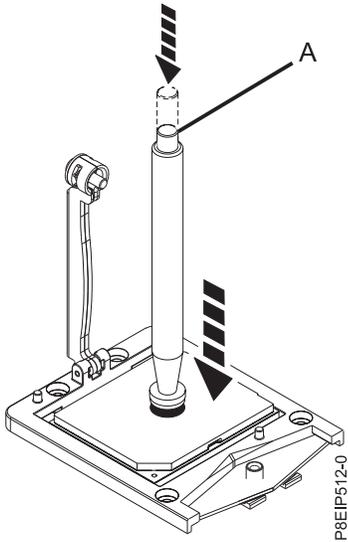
Ausbauwerkzeug auf das Systemprozessormodul herabsenken
